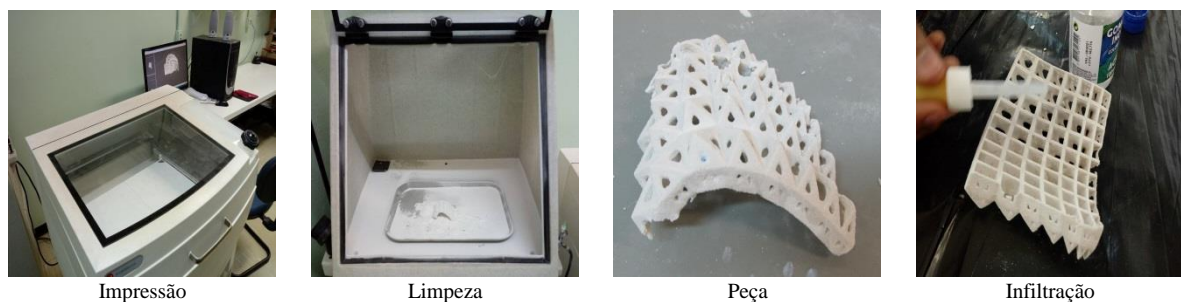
Teste de impressão 3D por fundição de pó ZCast.. Fonte: Própria.
